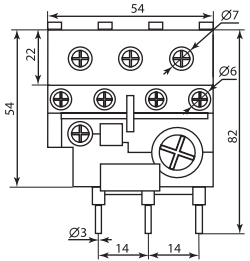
Габаритные и установочные размеры реле PTL-2053-M2
